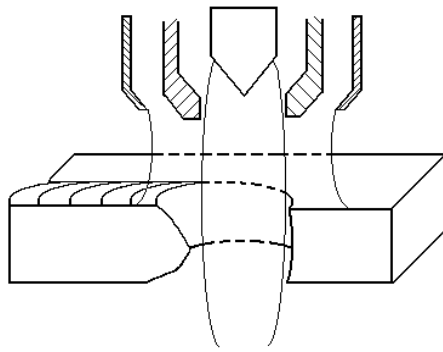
Técnica “keyhole” de soldagem (Walsh & Nunes Jr, 1989).
